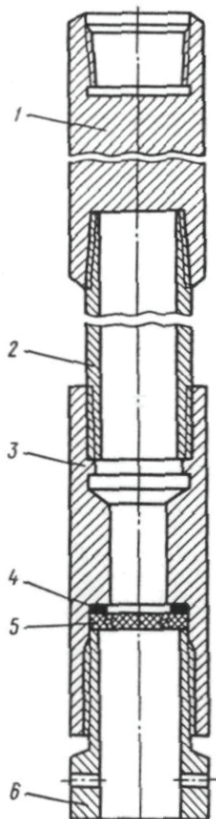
Пристрій для обробки свердловини методом імплозії [294]:
